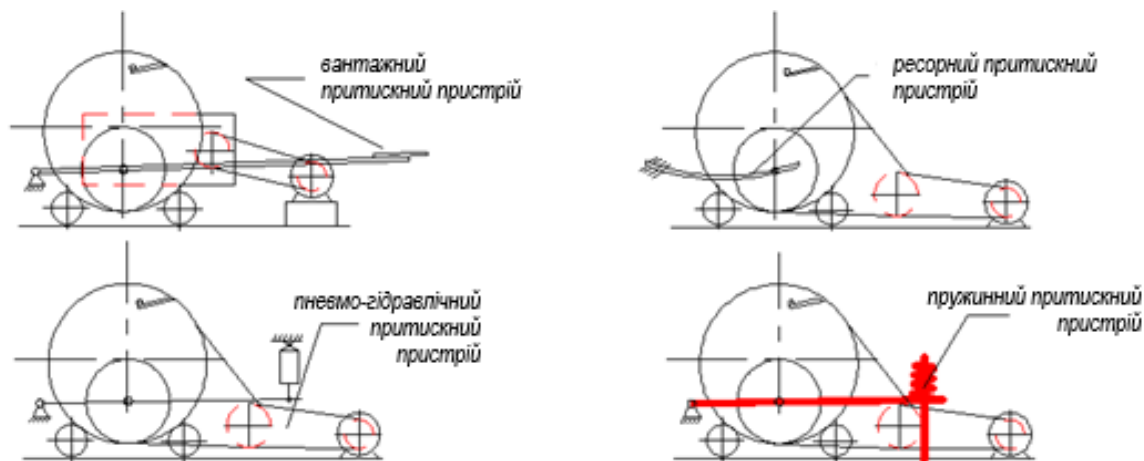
Схеми конструкцій притискних пристроїв
